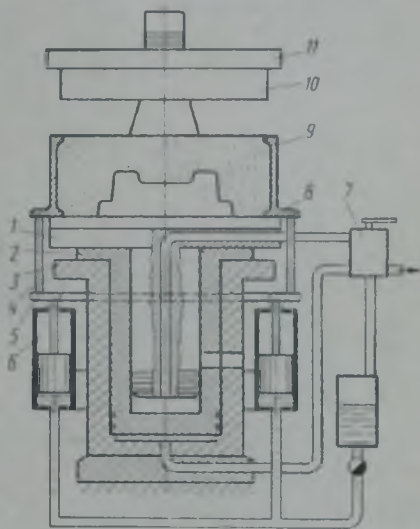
Схема работы встряхивающей формовочной машины с допрессовкой:
